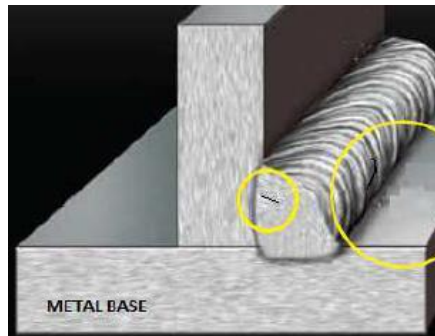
Grietas cordón de soldadura [4].
